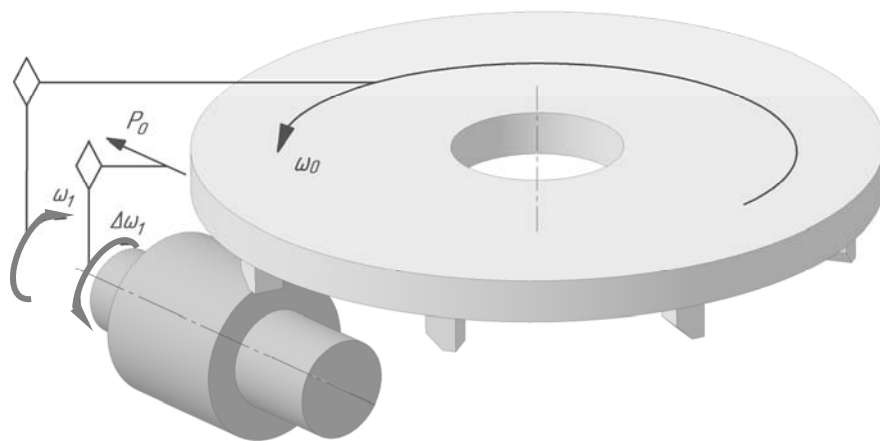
Схема формообразования витков червяка торцевой резцовой головкой при непрерывном делении
